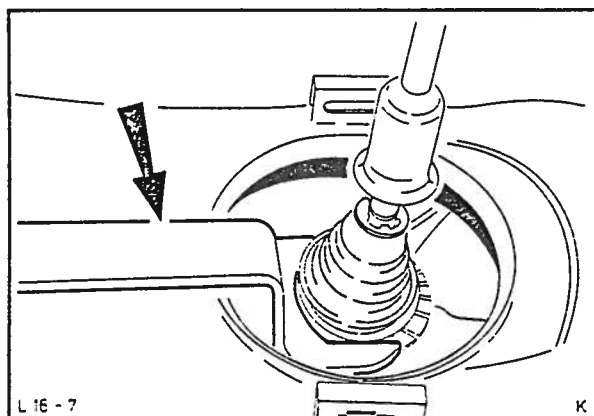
Demontering av gearspak med spesialverktøy 16-026.
